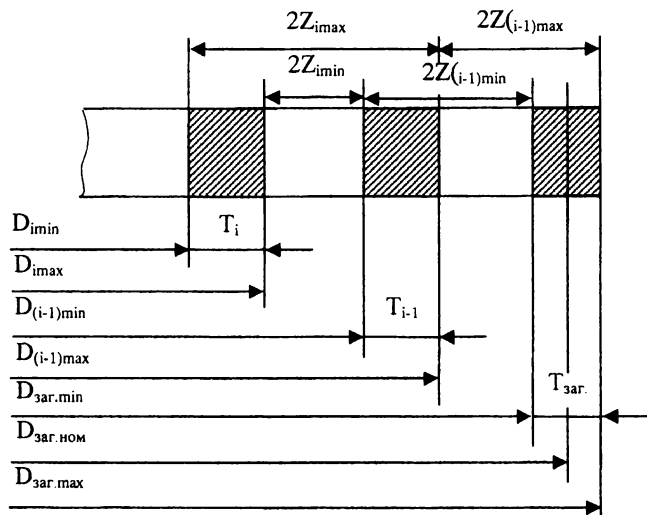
Схема графического расположения припусков и допусков на обработку наружной поверхности вала
